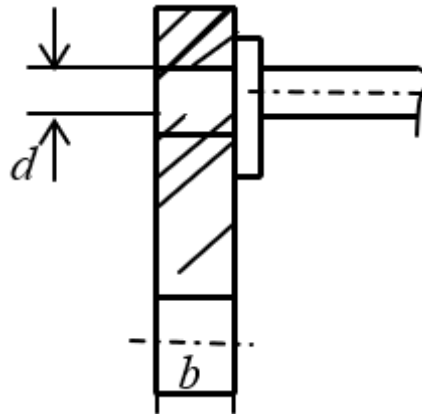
Схема склеивания зубчатого колеса с валом
